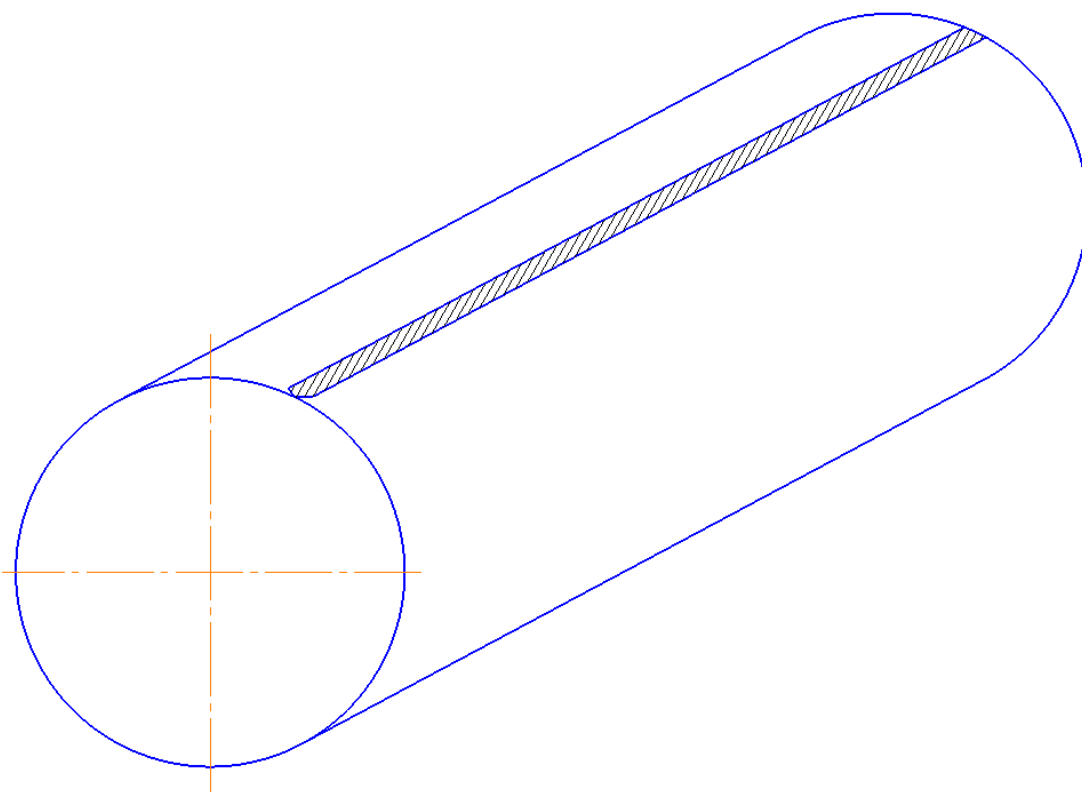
Эскиз операции сварки продольного шва
